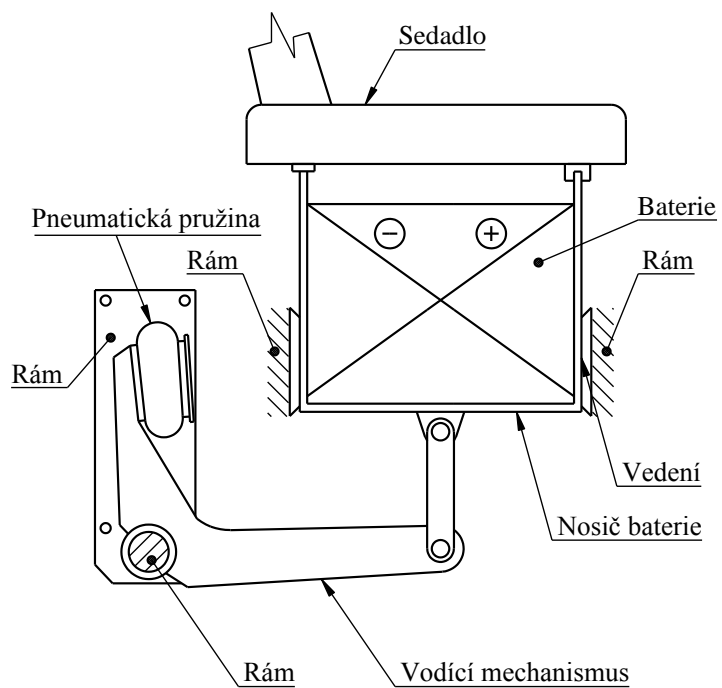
Konstrukční varianta 1 – odpružení sedadla
